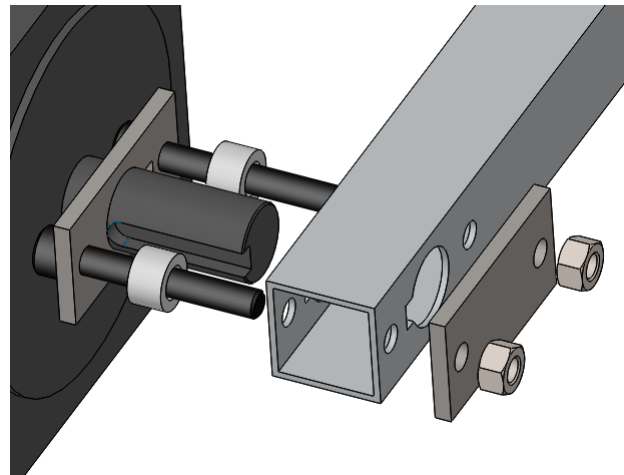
Vista explodida do acoplamento do elo superior com o motor.
